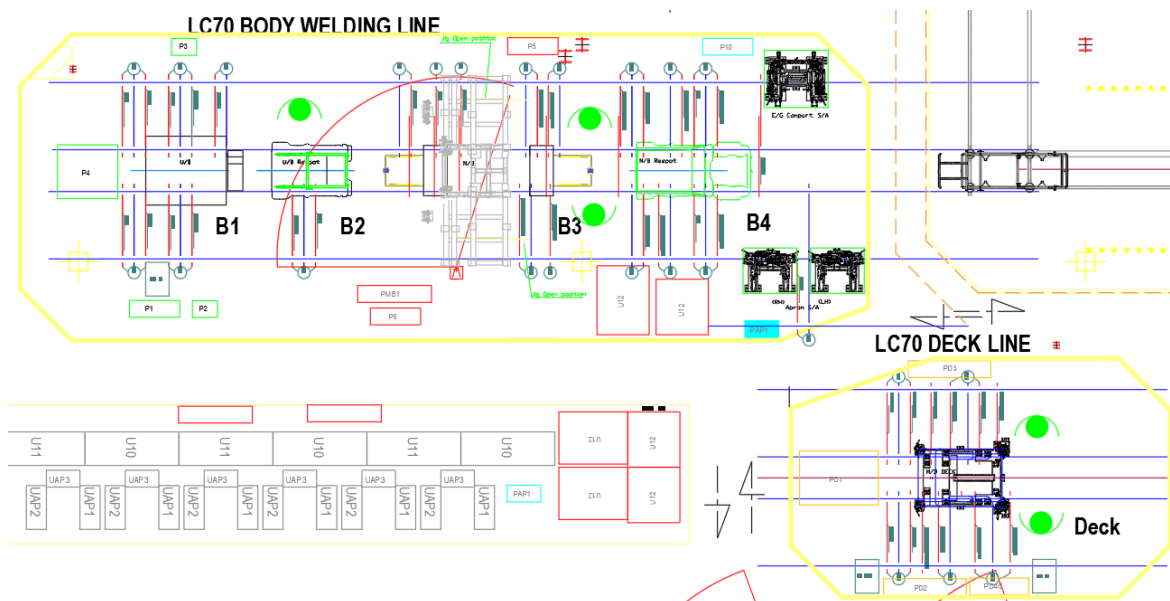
Linha de Soldadura *Body* e Linha de Soldadura *Deck* (Fonte: Toyota Caetano Portugal)
